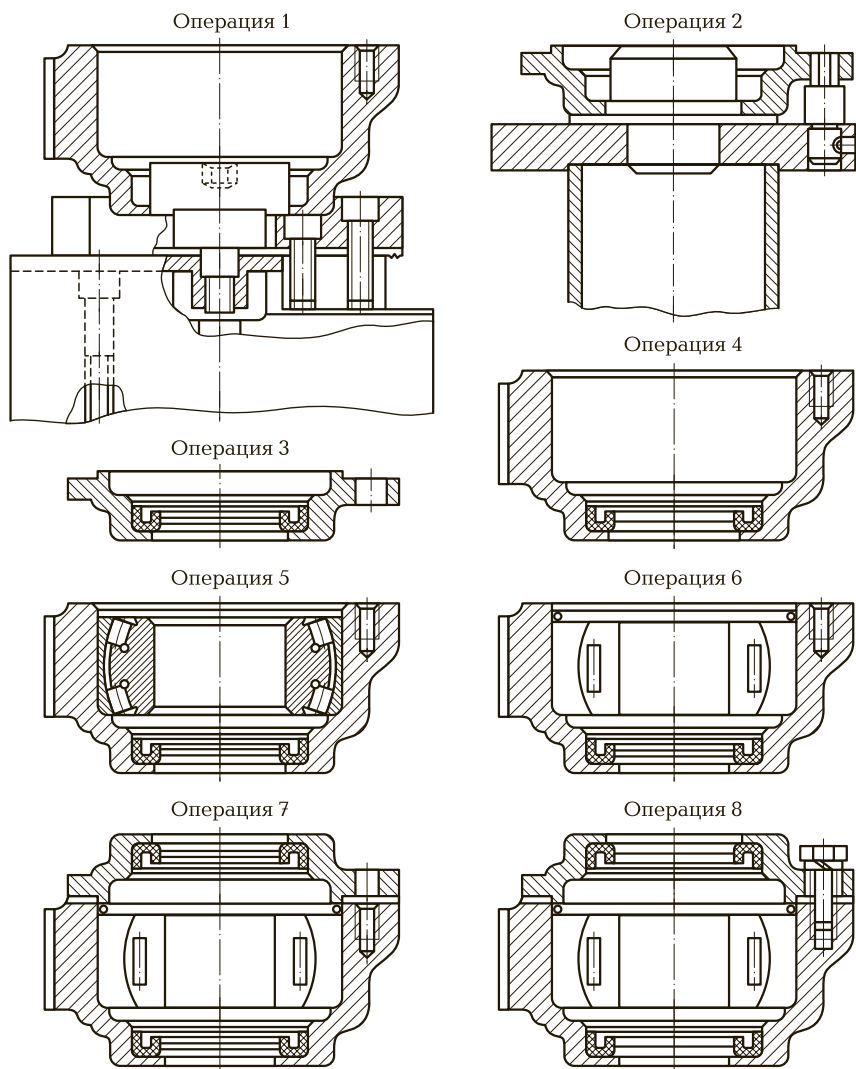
Эскизы выполнения операций сборки подшипникового узла на роботизированном сборочном комплексе
